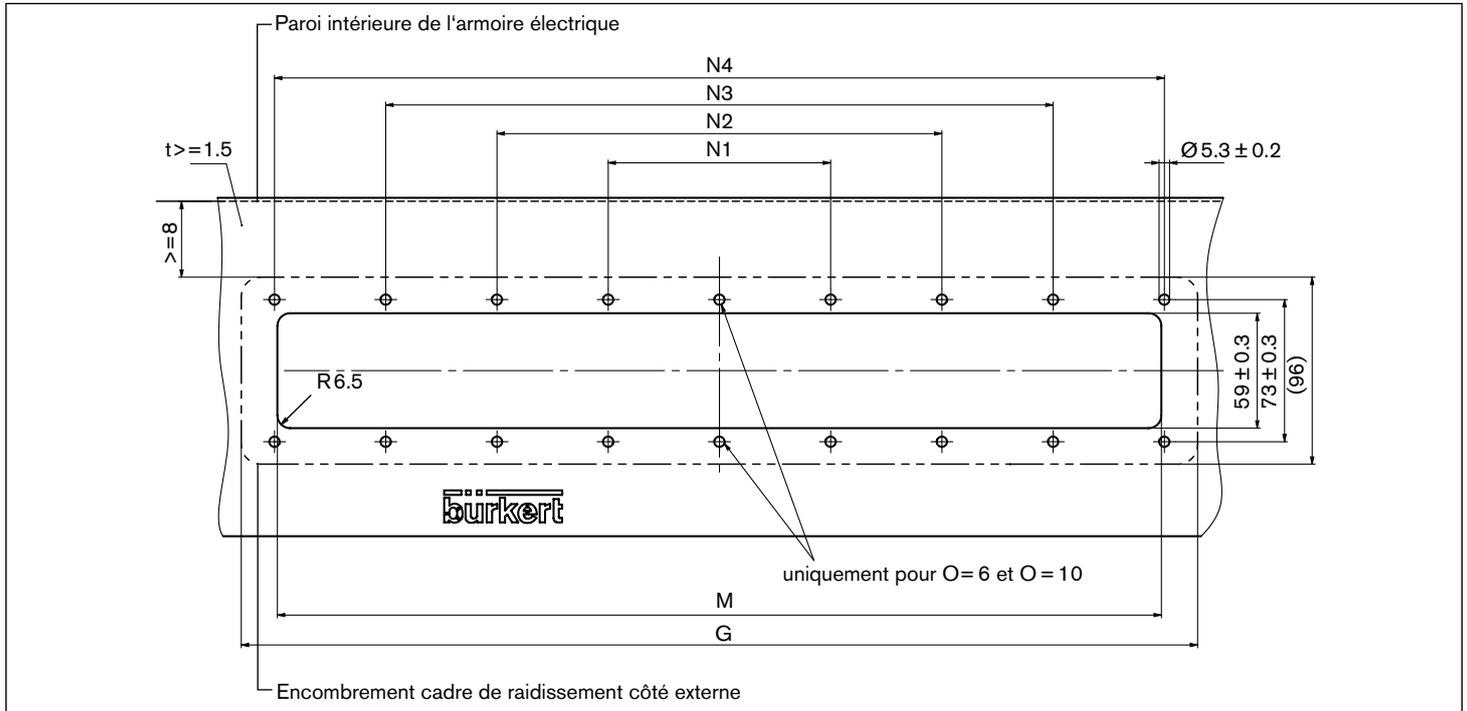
Dimensions des réseaux de brides pour AirLINE Quick – dimensions, voir « Tab. 1 », page 46
